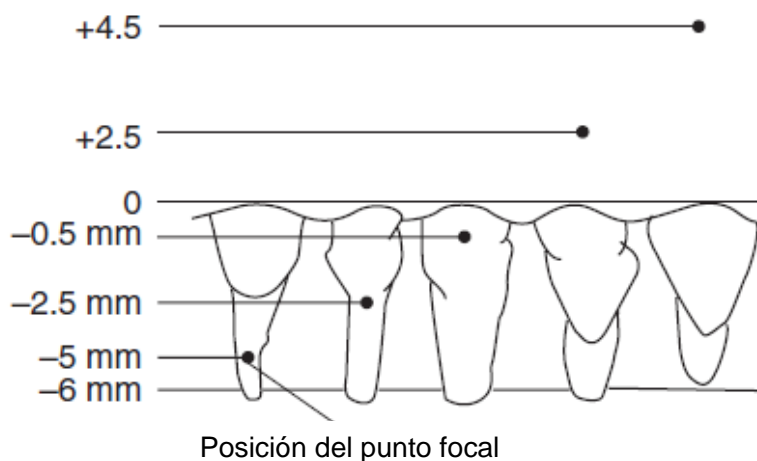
Perfiles transversales de soldadura láser de un acero inoxidable 310 en función de la posición focal del láser. [39]
